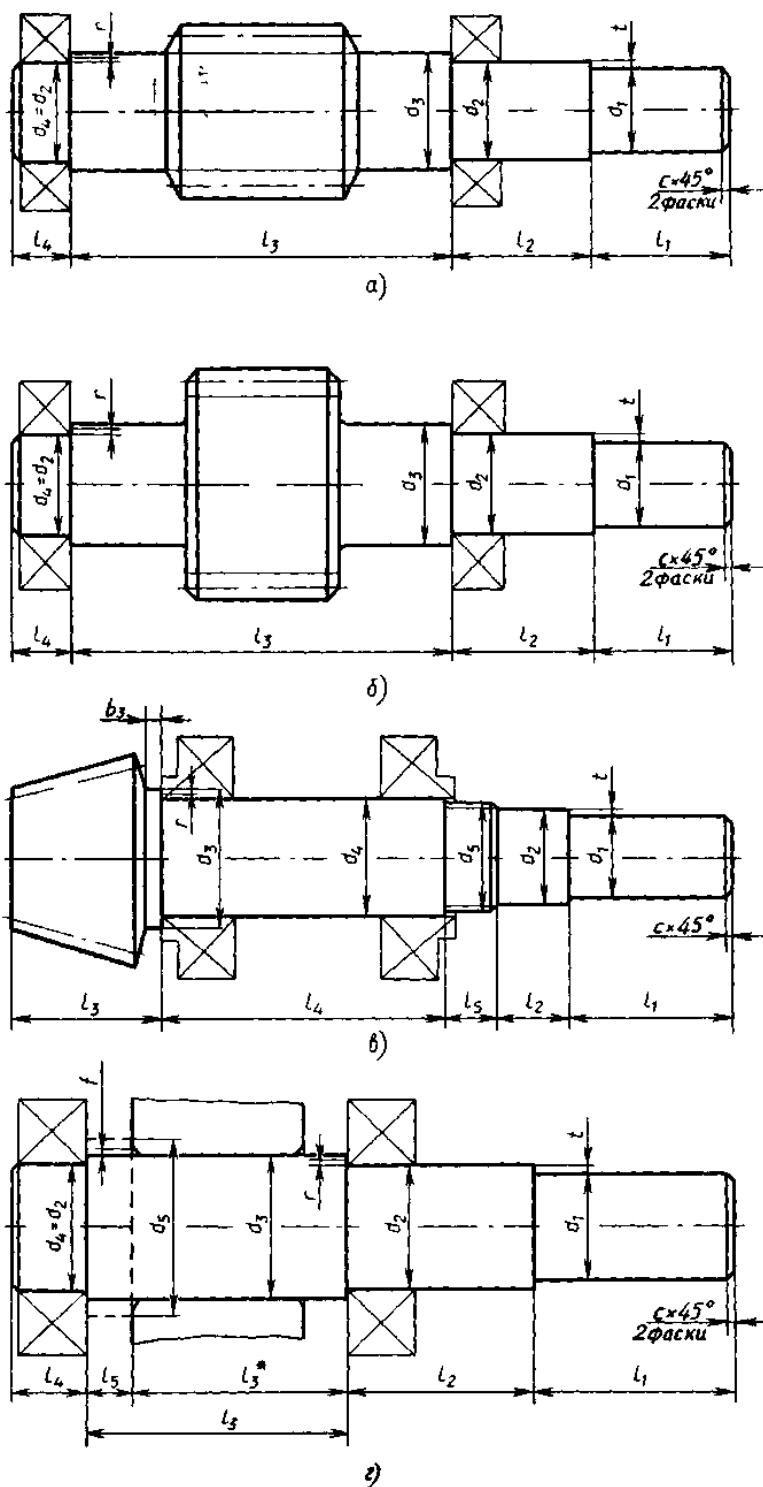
Типовые конструкции валов одноступенчатых редукторов: а - быстроходный-червячного; б - быстроходный цилиндрического; в - быстроходный-конического; г - тихоходный (l_3^* -в коническом редукторе)
